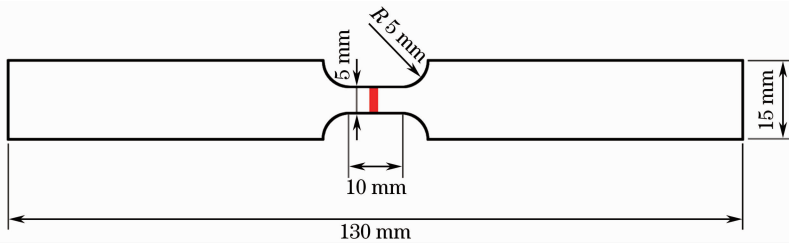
DP600 激光对接焊接接头拉伸试样尺寸
